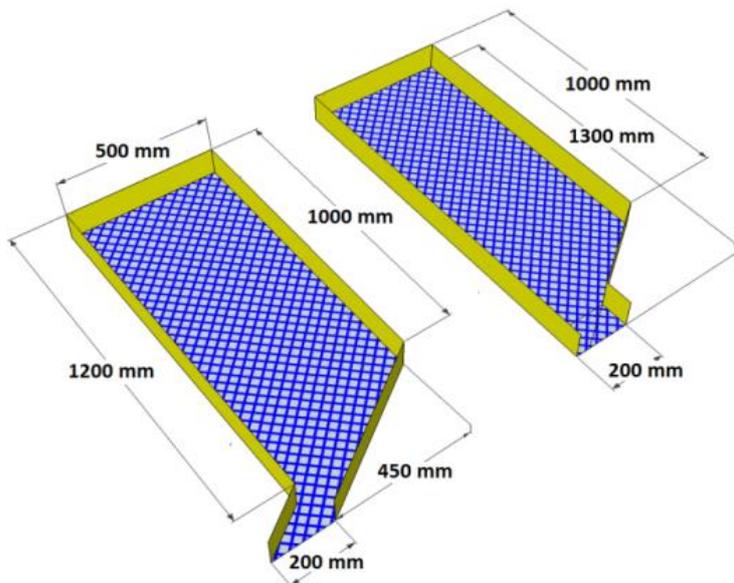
Opções de formato para as peneiras de separação de material grosseiro.
